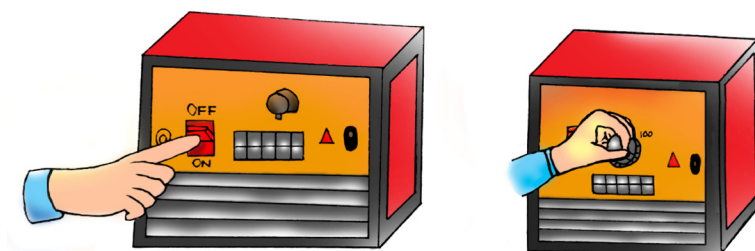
Encendido y regulado de intensidad de soldadora
